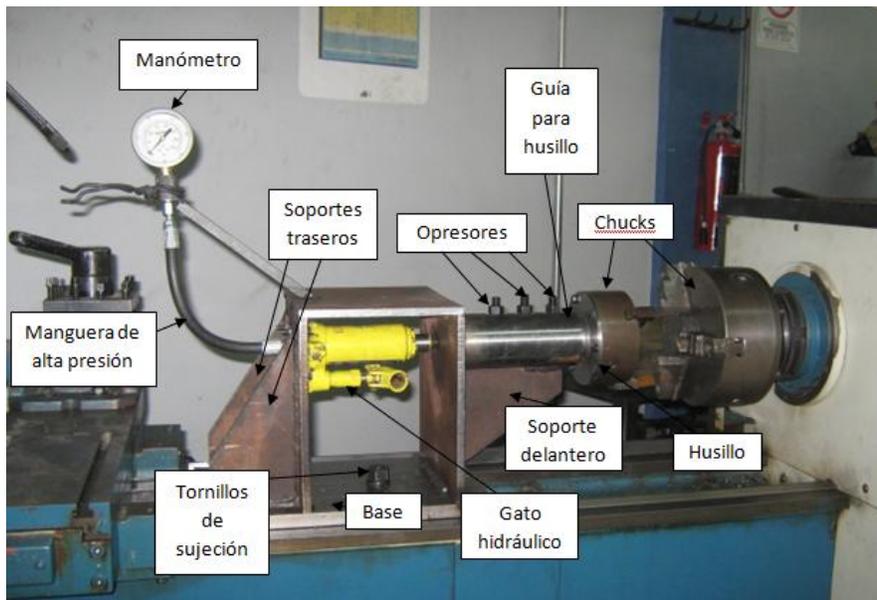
Partes principales del dispositivo implementado para la soldadura por fricción
